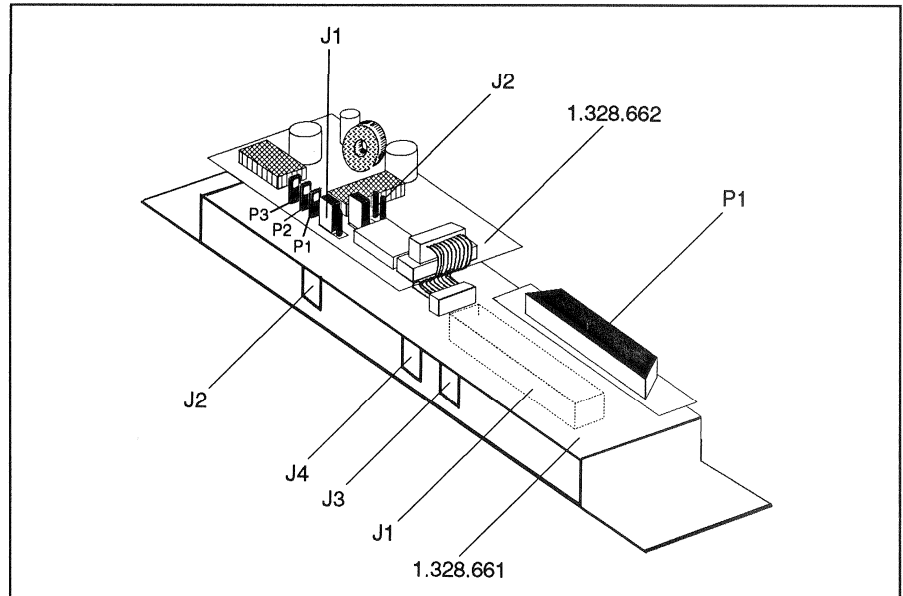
Jumper und Anschlüsse der parallelen Fernbedienung
